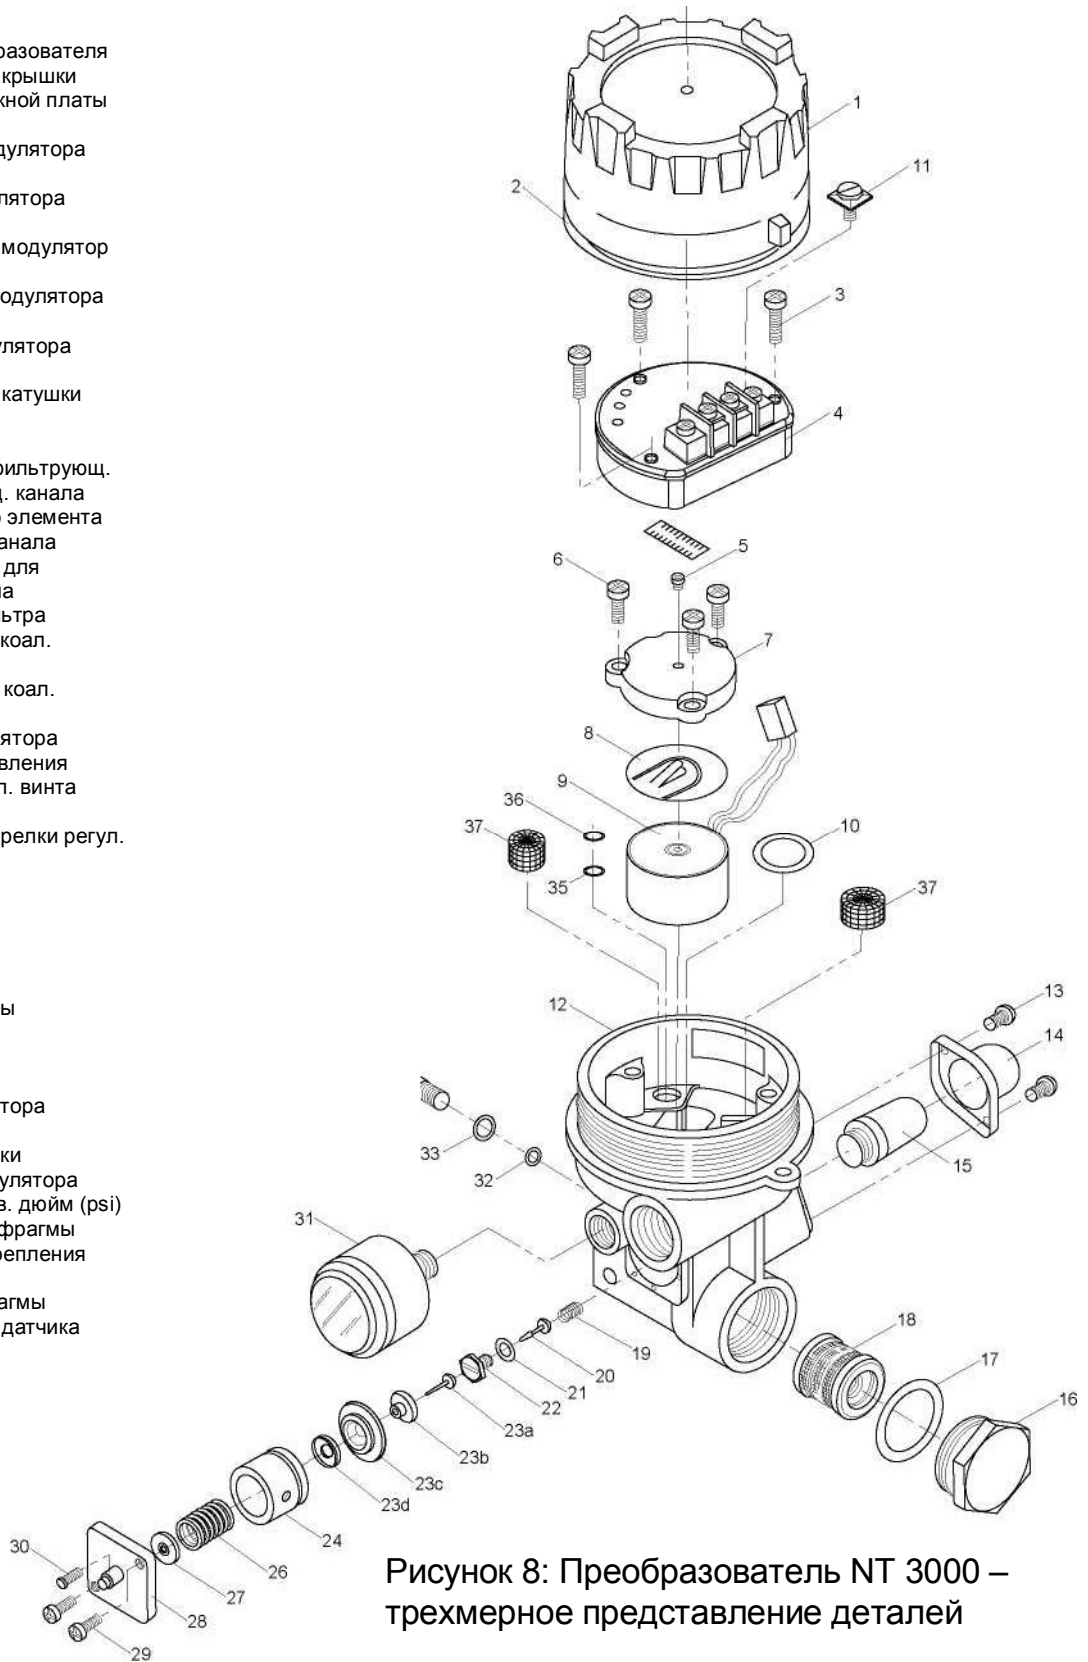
Преобразователь NT 3000 – трехмерное представление деталей
